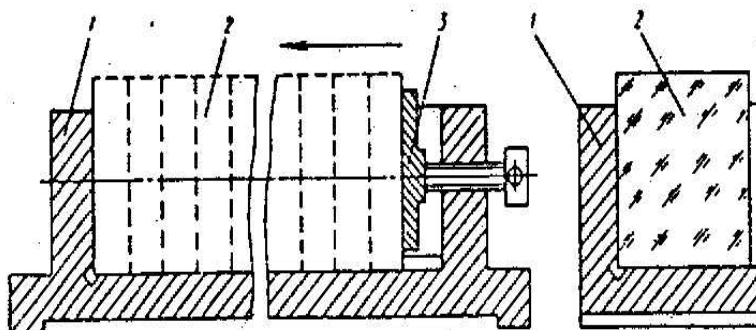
Приспособление для обработки торцов заготовок некруглой формы
